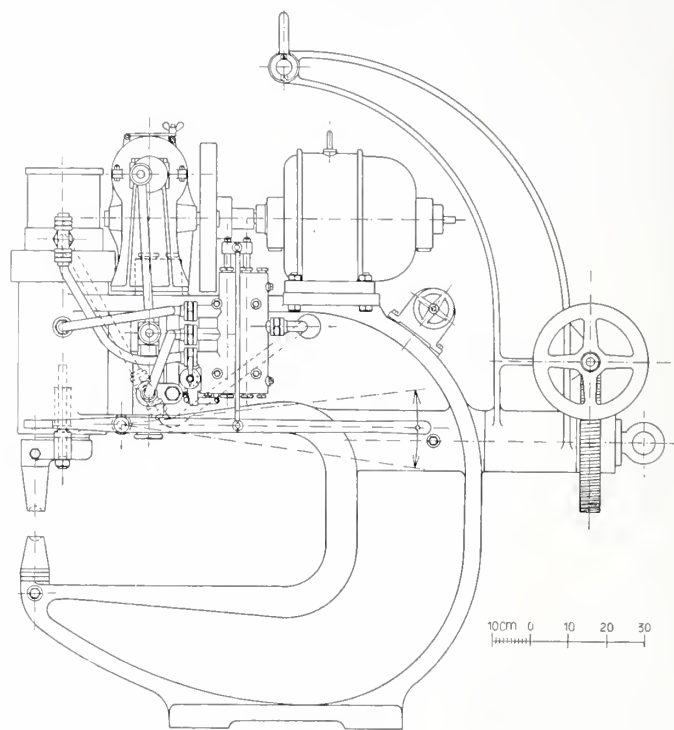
Geometrische Ansicht der Nietmaschine. — 1 : 20.
